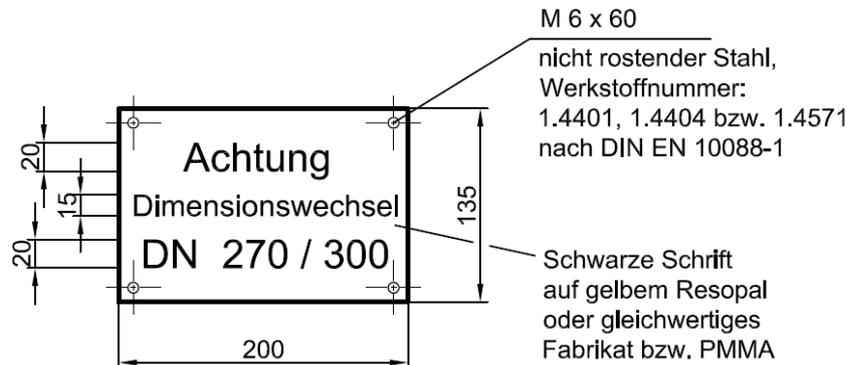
Hinweisschild für Dimensionswechsel DN 270/300
